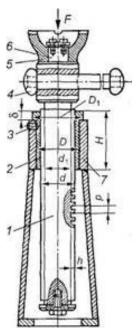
Винтовой домкрат: 1 — винт; 2 — гайка; 3 — стопорный винт; 4 — рукоятка; 5 — чашка домкрата; 6 — шип, 7 — корпус
